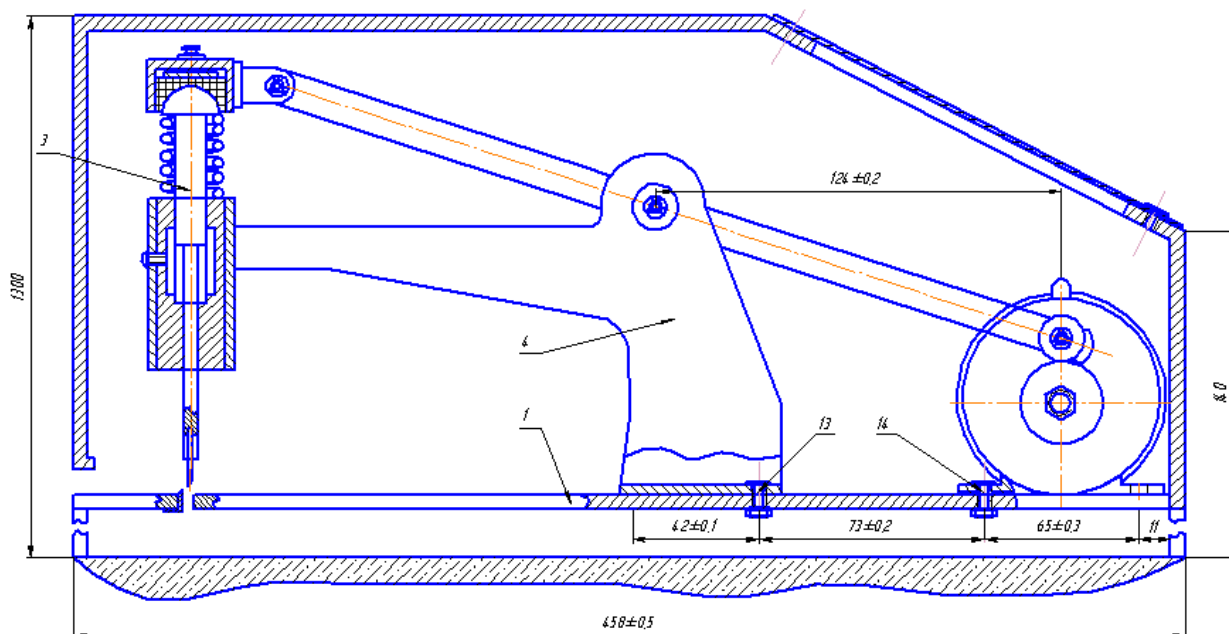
Схема приспособления для вырезания прокладок
